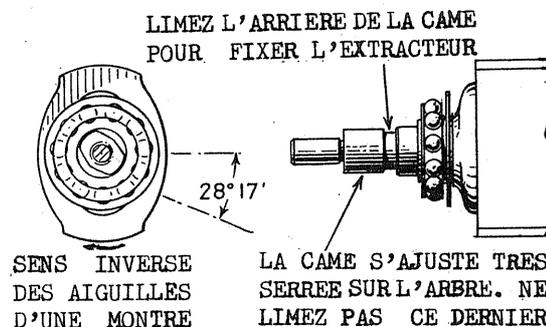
ENDOITS OU ON PEUT LIMER LE ROTOR POUR ENLEVER LA CAME.
